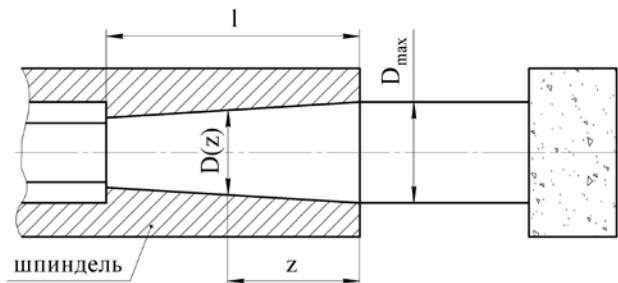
Розрахункова схема стикового з'єднання „шпиндель - оправка”
